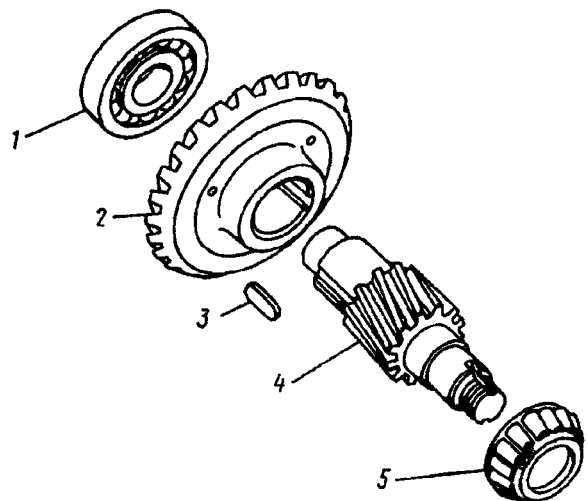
Узел ведущего цилиндрического зубчатого колеса в сборе:
